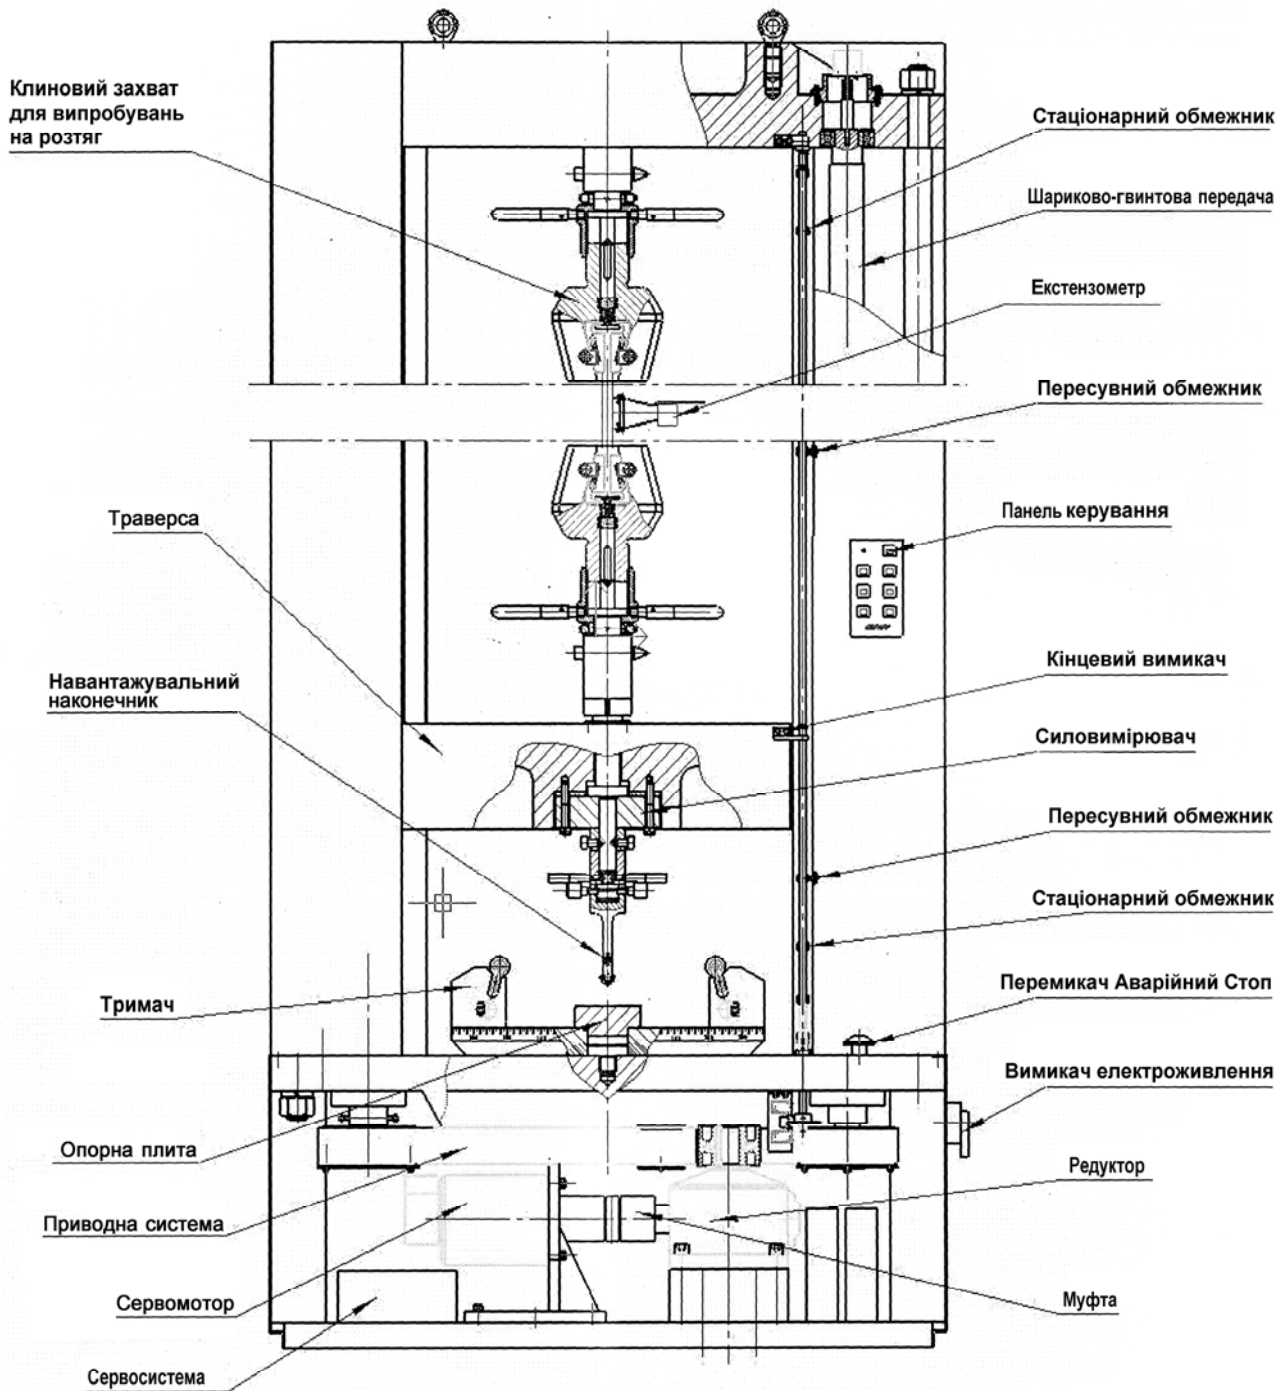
Принципова схема механічної частини універсальної іспитової машини SANS CMT2503
